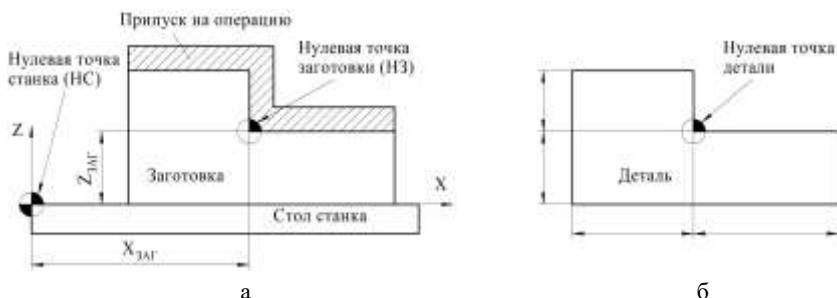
Нулевые точки: а – заготовки на станке; б – детали с САПР
